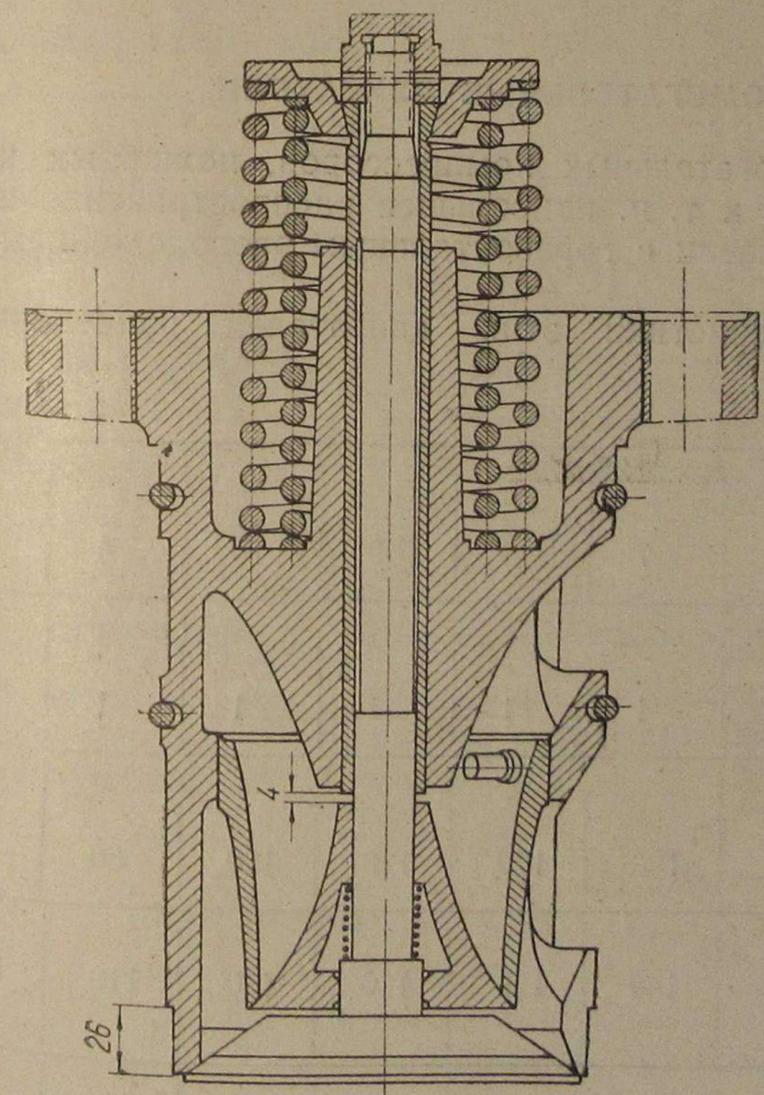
Всасывающий клапан газового двигателя 375 л. с.
